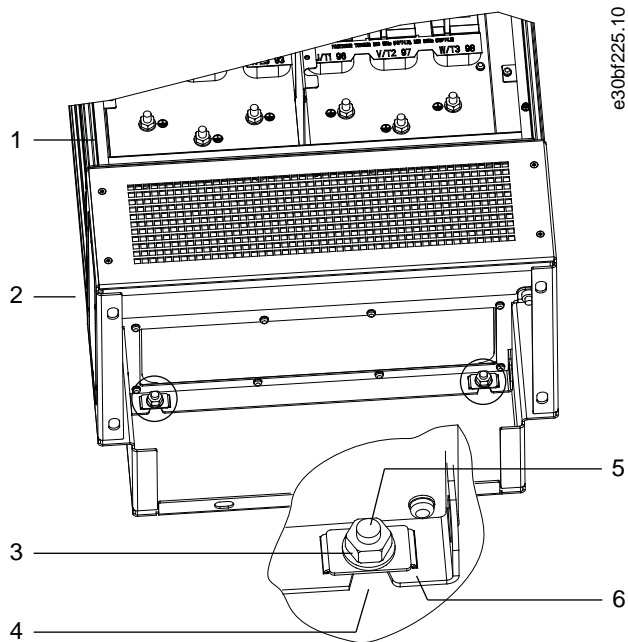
Montagepunkte für Befestigung der Gehäuserückseite am Sockel
